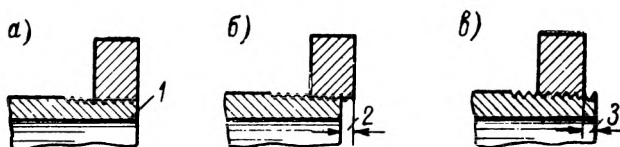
Измерение наружной конической резьбы: а — теоретический размер; б — максимальный размер; в — минимальный размер. 1 — плоскость совпадения; 2 — на $1\frac{1}{2}$ оборота больше; 3 — на $1\frac{1}{2}$ оборота меньше.
